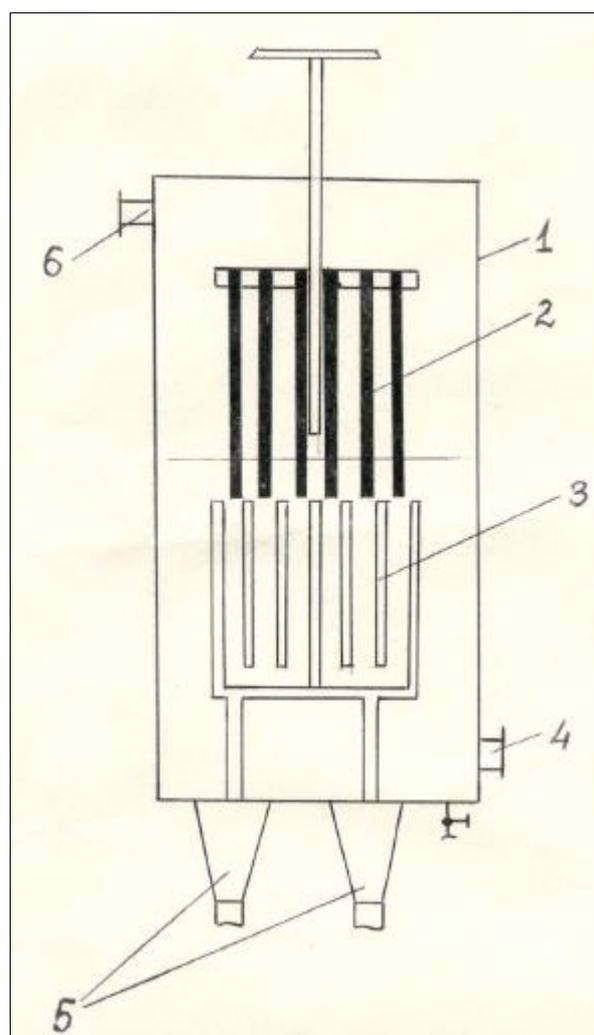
Схема электрокотла: 1 – корпус; 2 – пакет диэлектрических пластинок; 3 – патрубок для входа нагреваемой воды; 5 – вводы электропитания; 6 – патрубок для выхода нагретой воды
